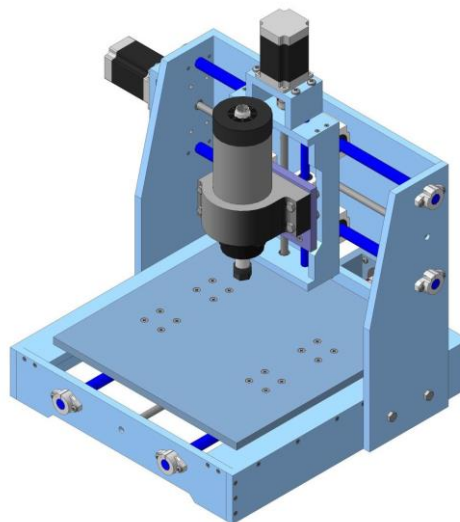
Спроектований вертикально-фрезерний верстат із ЧПУ.
